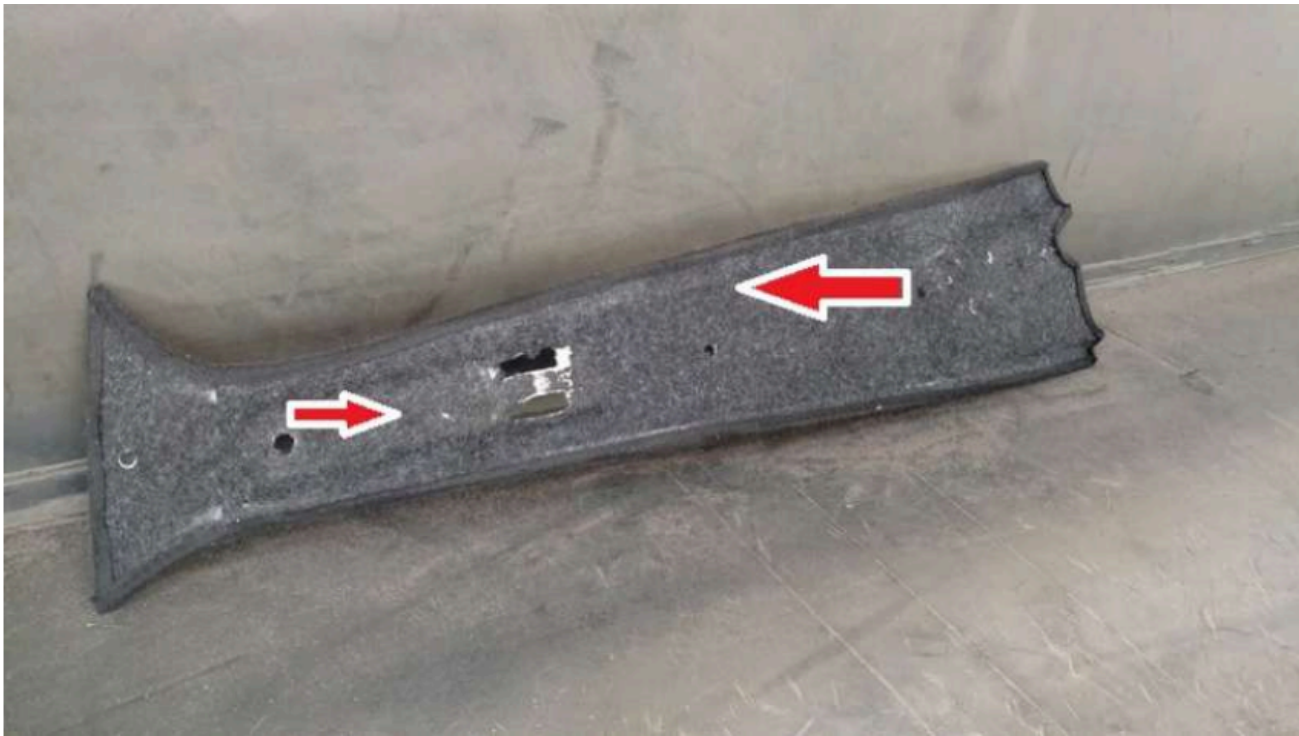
Detalhe do carpete aplicado na face oposta da chapa de aço.
